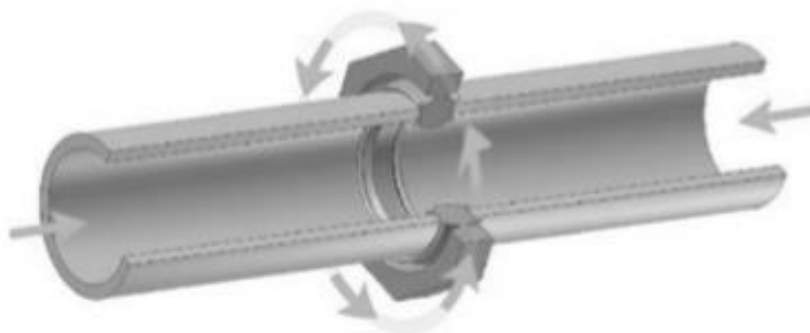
Desenho esquemático da solda por fricção com anel intermediário (17).
